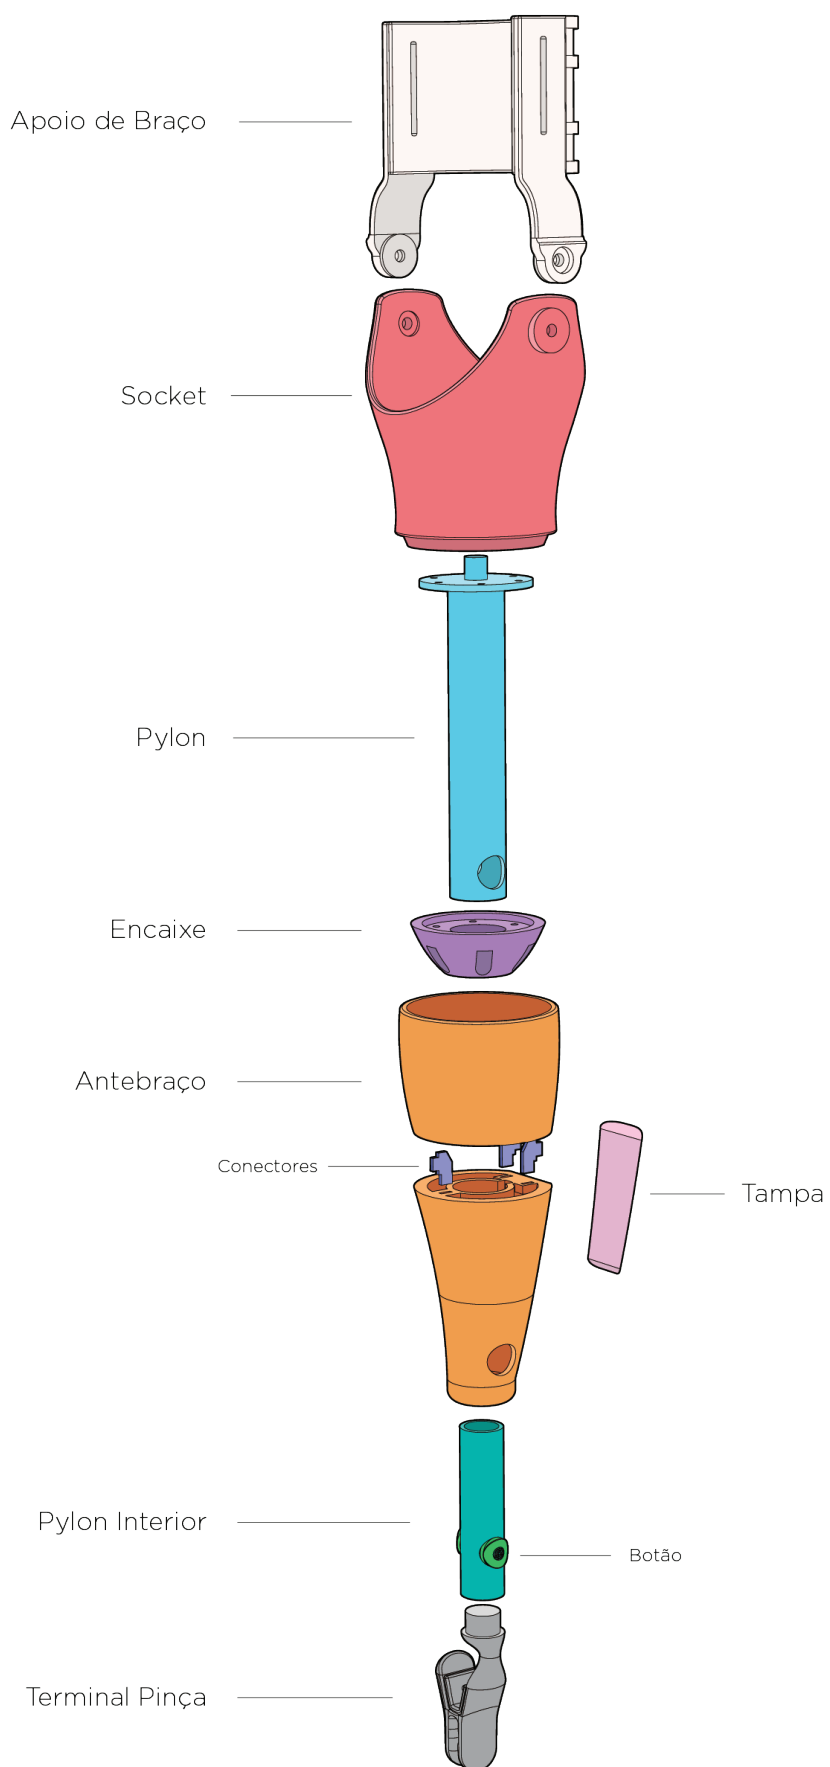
Perspectiva Explodida dos componentes da prótese; *Fonte: Investigador (2016).
